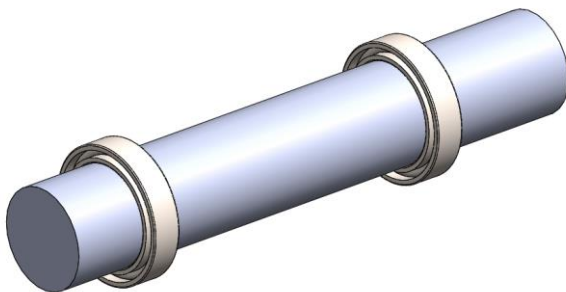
Diseño en solid works. Rodamientos 6203 instalados en una flecha
